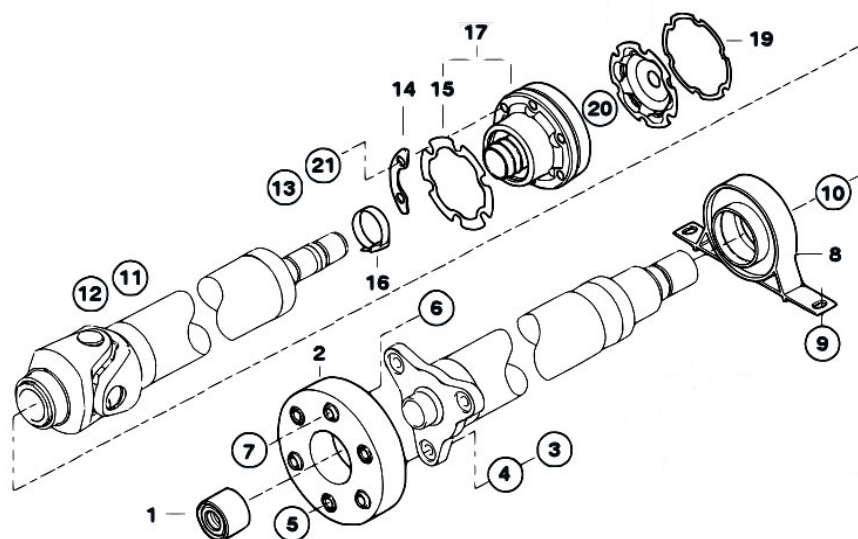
Koncepce pohonu s motorem vpředu a pohonem zadních kol [12]
